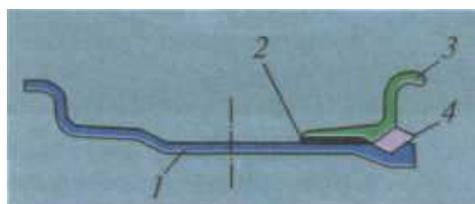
Установка запорного кольца при монтаже шины на разборный обод
